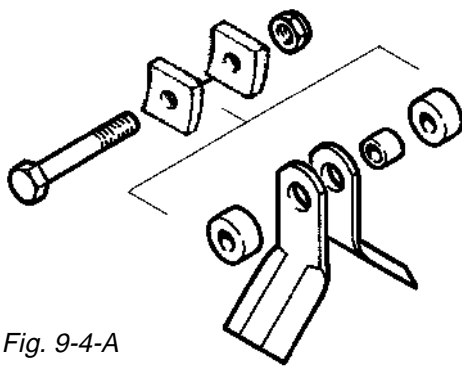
Montaggio coltelli FL - FL knives assembly
